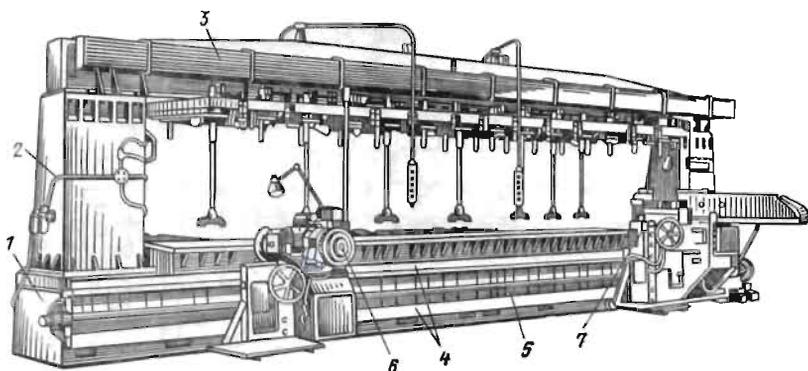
Фрезерно-обрезной станок ФОЛ-2М
